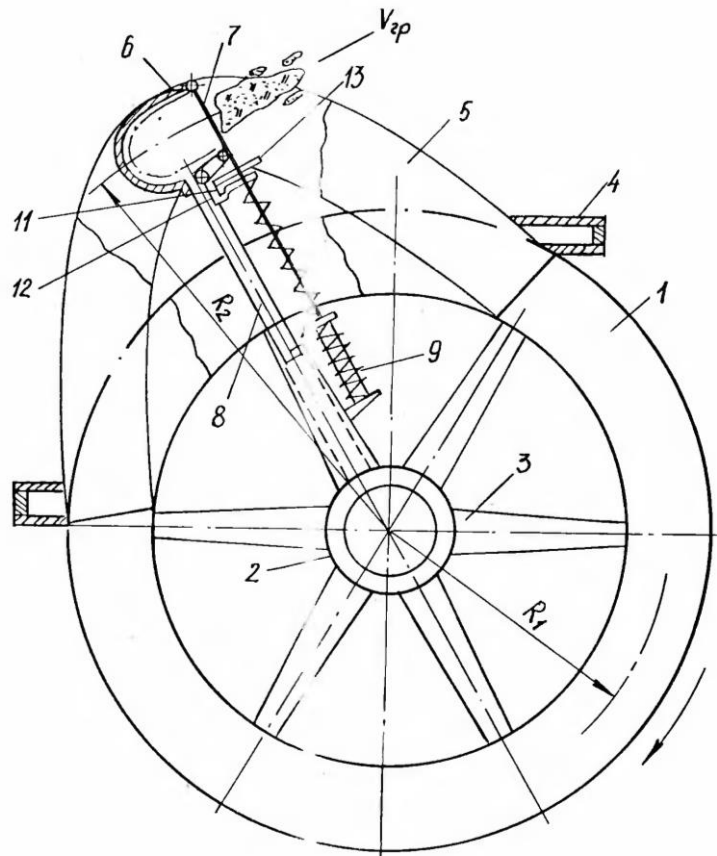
Метальник з обичайкою параболічної форми
